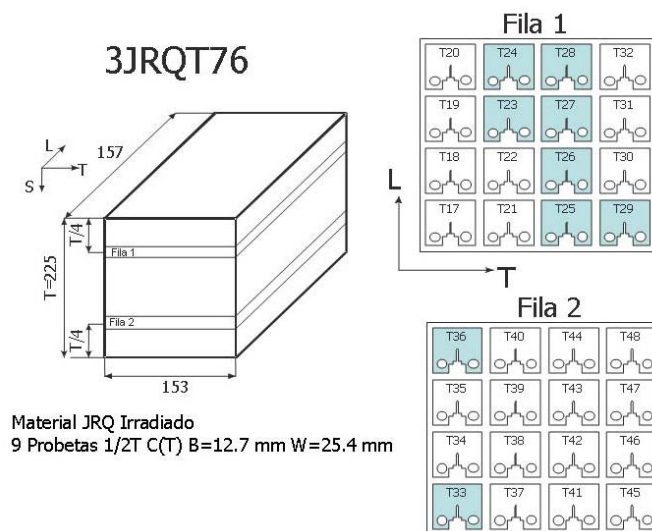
Material JRQ Irradiado. Bloque 3JRQT76. Mecanizado de probetas
